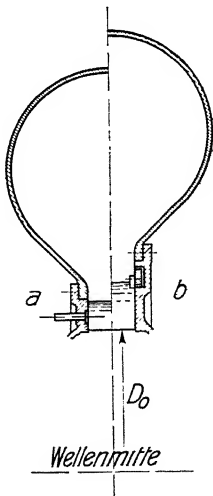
Gehäusequerschnitte mit kurzer ( $a$ ) und mit langer Leitschaufel ( $b$ ).
